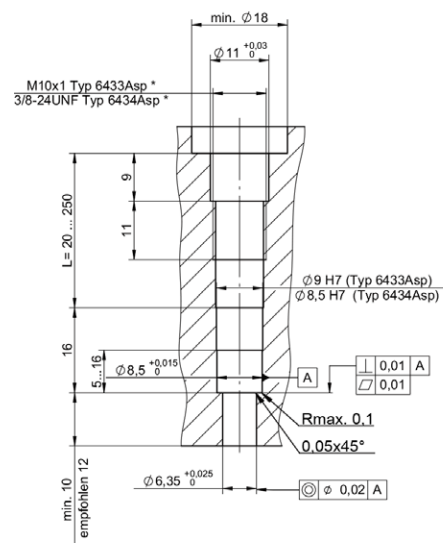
Bohrung für Einbau mit Montagehülse, kundenspezifisch
